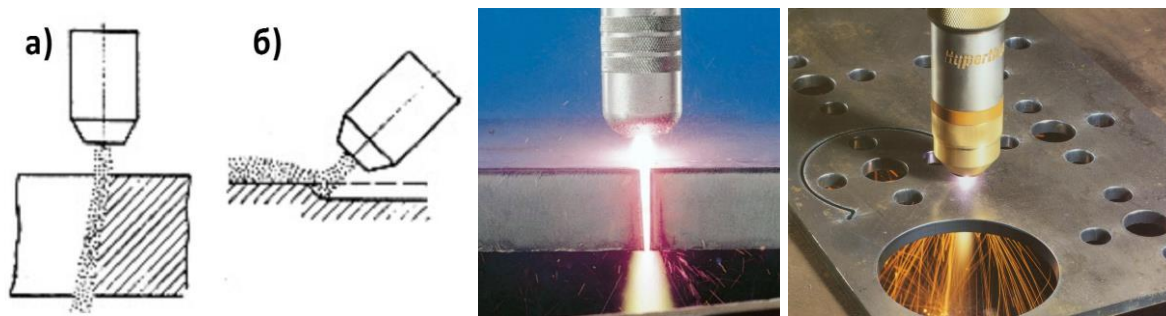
Схема та зовнішній вигляд плазмового різання металу
